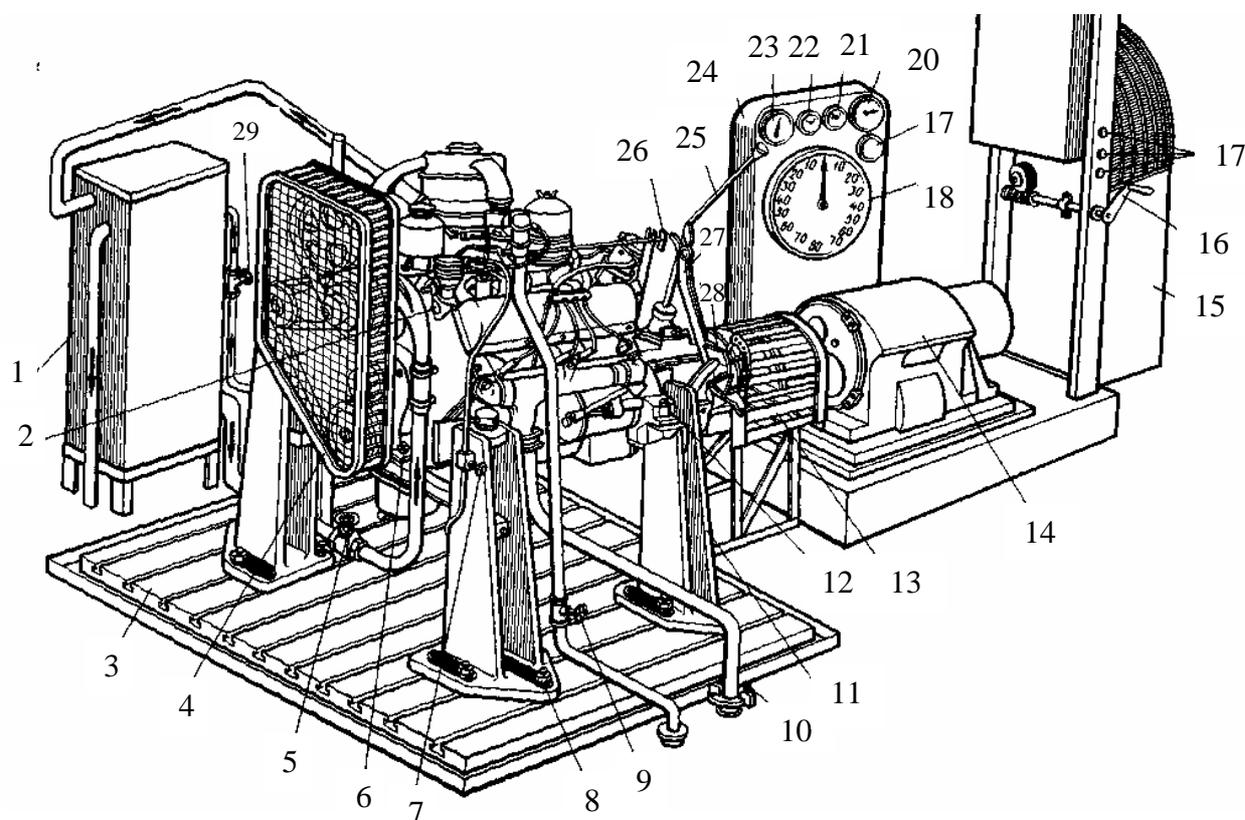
Стенд для обкатки и испытания двигателей: 1 – бак; 2 – двигатель; 3 – плита; 4 и 13 – решетки; 5, 9 и 29 – вентили; 6, 8 и 12 – элементы крепления двигателя; 7 – кран; 10 – элементы крепления газоотводной трубы; 11 – стойка; 14 – электромашин; 15 – реостат; 16 – рукоятка управления реостатом; 17 – кнопки; 18 – шкала; 19 – сигнализатор; 20 – тахометр; 21 и 22 – термометры; 23 – манометр; 24 – корпус; 25 – рычаг коробки передач; 26 – тяга; 27 – рычаг ручного тормоза; 28 – педаль
